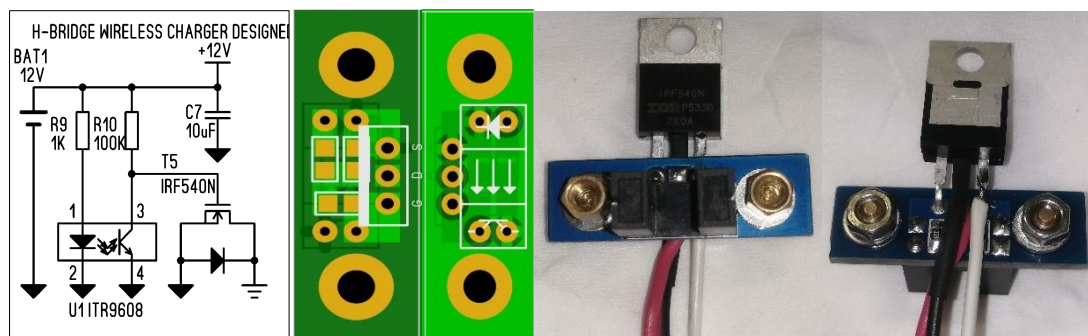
槽型光耦 U1 感应信号电路原理图、PCB 设计图及实物正反面装配图
